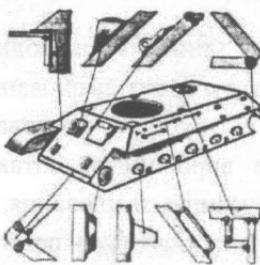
Схема зварювання корпуса танка Т-34
